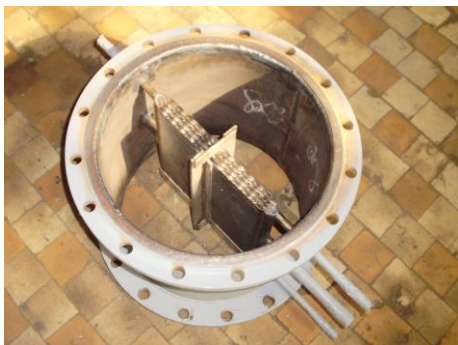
Фрагменты греющей камеры экспериментального выпарного аппарата со сварной пластинчатой греющей камерой
